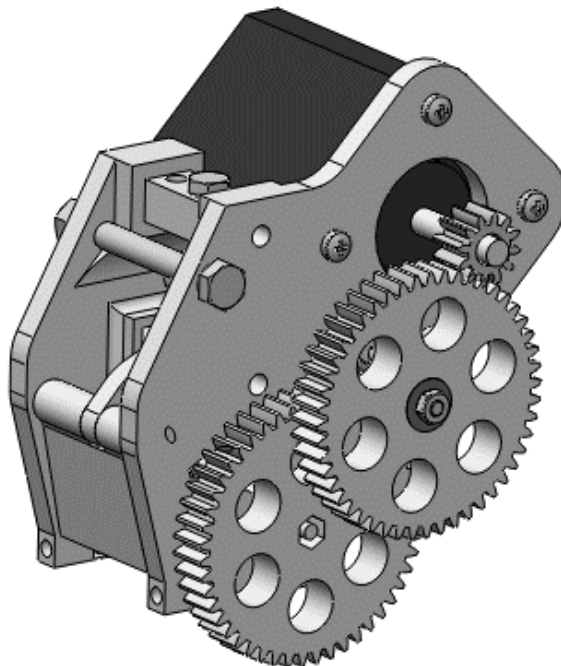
Extrusor de engranajes pivotantes (Versión 02)
